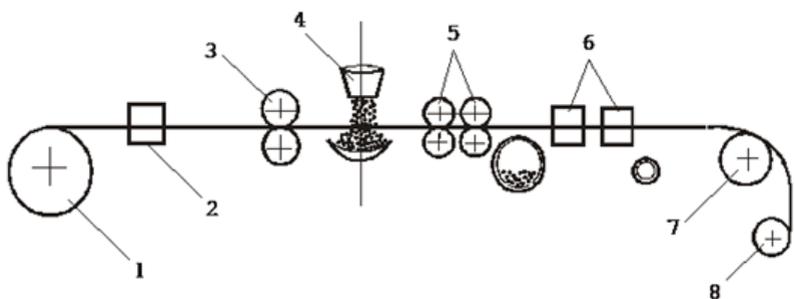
Схема процесса изготовления порошковой проволоки:
